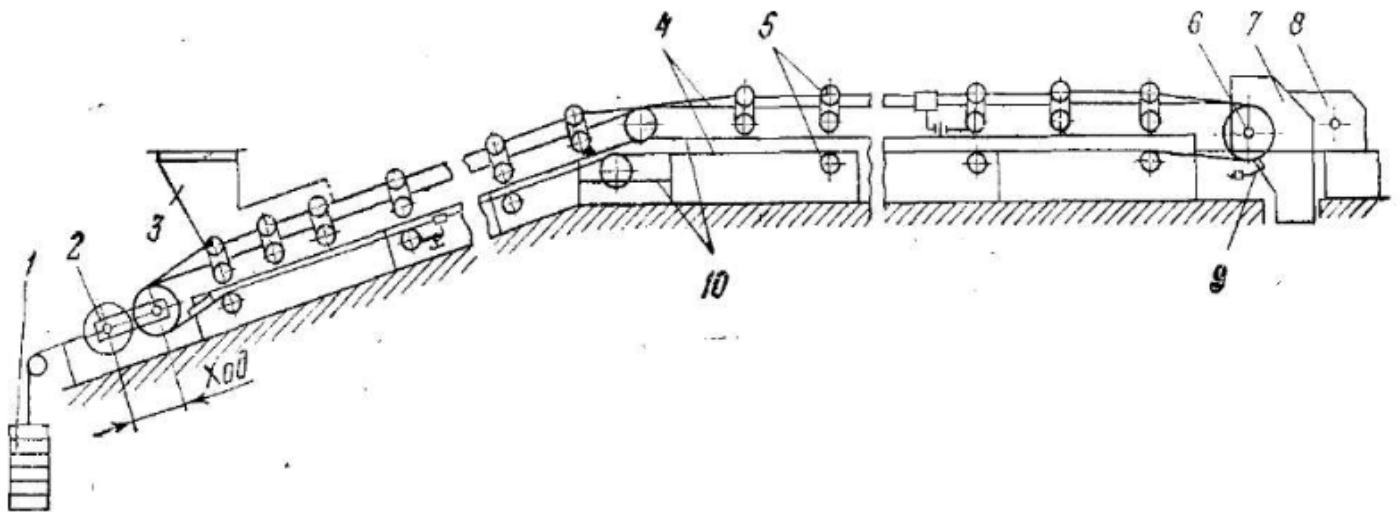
Схематичне зображення лінії стрічкового конвеєра: 1 - натяжна станція; 2 - барабан натяжної станції; 3 - завантажувальний пристрій; 4 - стрічка; 5 - роликові опори; 6 - приводний барабан; 7 - розвантажувальний пристрій; 8 - приводна станція; 9 - очисний пристрій; 10 - рама
